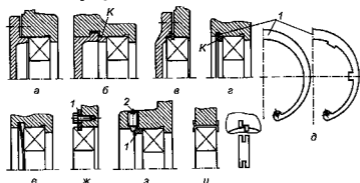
Способы крепления подшипников качения в корпусе:
